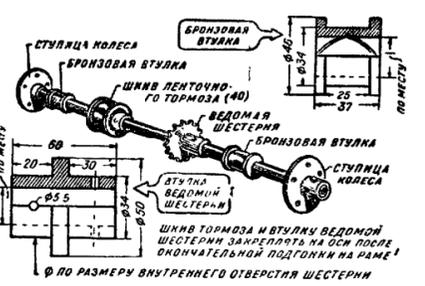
Задняя ось с деталями. В таком виде задняя ось устанавливается на раму. Сверлить в оси отверстия для болтов, крепящих шкив тормоза и втулку ведомой шестерни, следует после окончательной подгонки и регулировки тормозной тяги и моторной цепи на раме.
